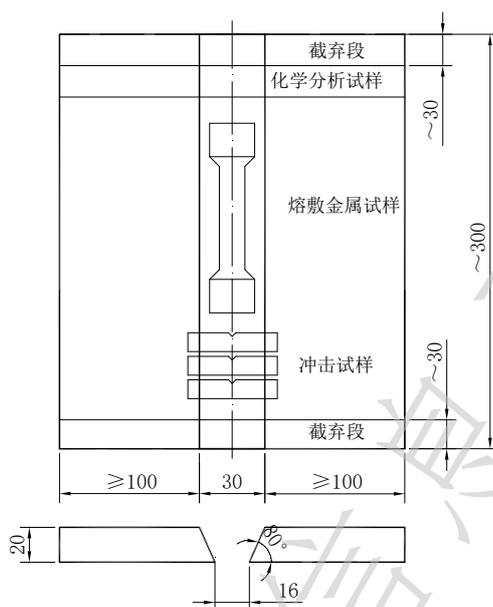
锅炉及受压容器对接焊试件的取样位置
